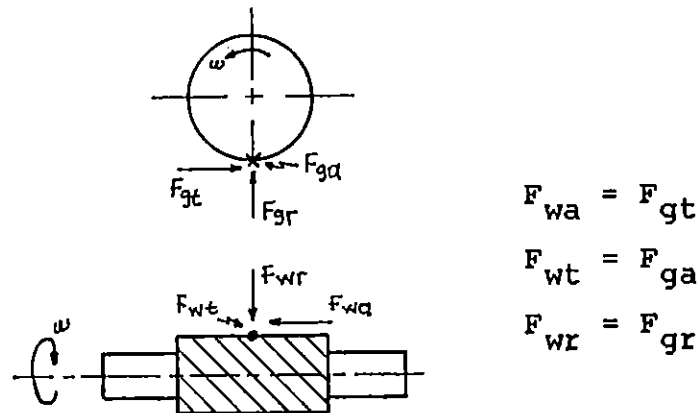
Esquema de fuerzas en el engrane y el tornillo.
